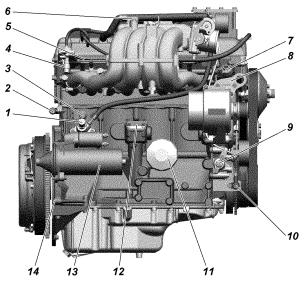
Motor ZMZ-40911 (vista derecha):
